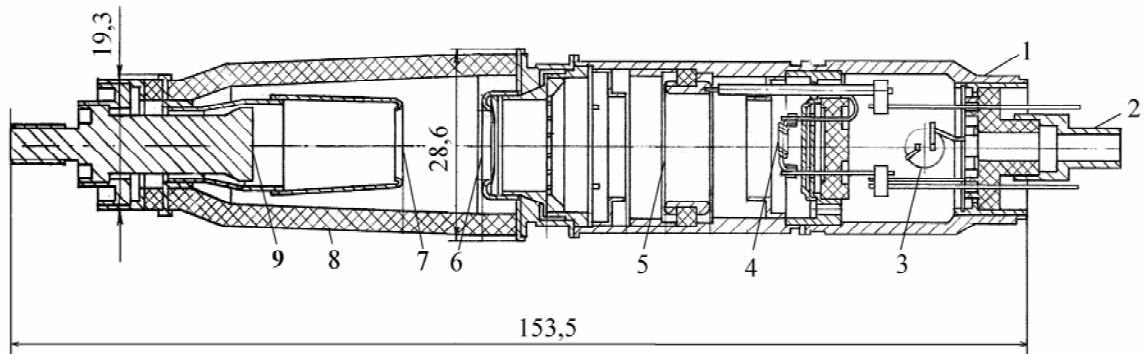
Прискорювальна нейтронна трубка НТГ-2М (схематичний розтин): 1 - корпус; 2 - штангель; 3 - сховище тритій-дейтерієвої суміші; 4 - катод джерела іонів; 5 - анод джерела іонів; 6 - екстрактор; 7 - антидинатронний електрод; 8 - високовольний ізолятор; 9 - титанова мішень.
